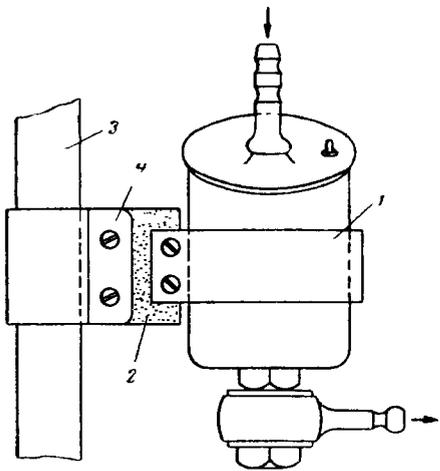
Схема крепления поплавковой камеры отдельно от смесительной: 1—хомутки обжима поплавковой камеры; 2—упругая деритовая диафрагма; 3—труба рамы мотоцикла; 4—хомутки крепления поплавковой камеры на раме мотоцикла.
